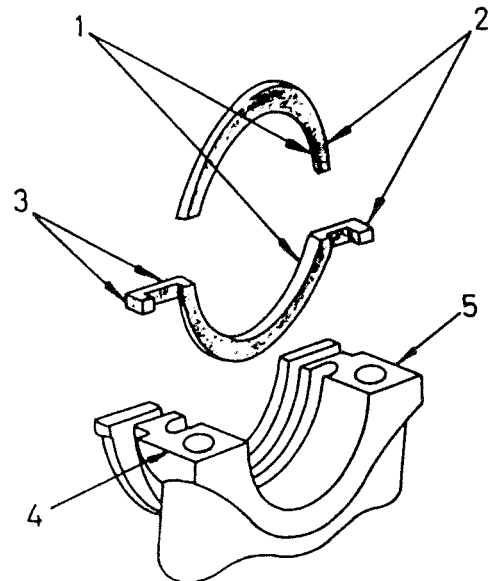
Die Teile des hinteren Hauptlagerdeckels mit dem Öldichtring
